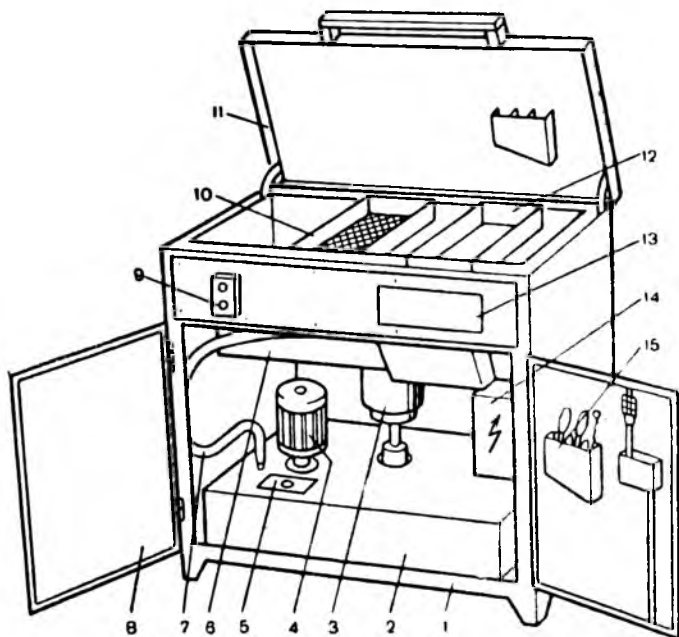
Установка ОМ-4990Б-ГОСНИТИ для мойки деталей:
